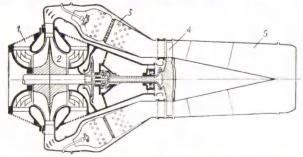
Схема турбореантивного двигателя: 1- входная часть; 2- компрессор; 3- камера сгорания; 4- турбина; 5- реантивное сопло.
